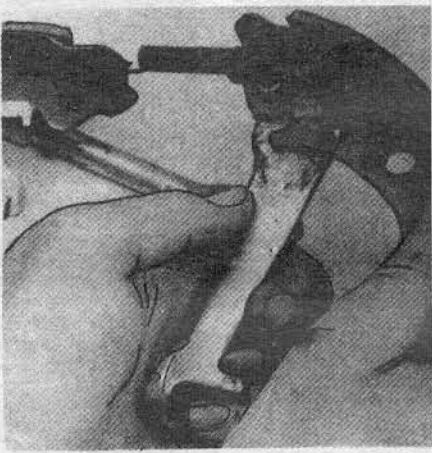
е Покачивая рычаг стояночного тормоза освободите серьгу регулировочного болта из его канавки на ведомой колодке. Разъедините колодки.
